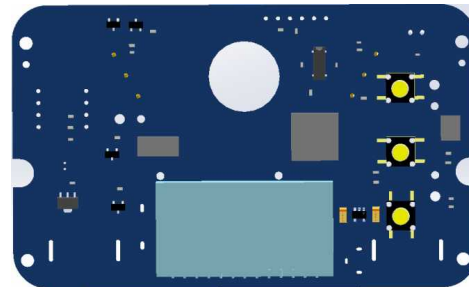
Solidworks에서 변환된 PCB 스텝 파일 결과
